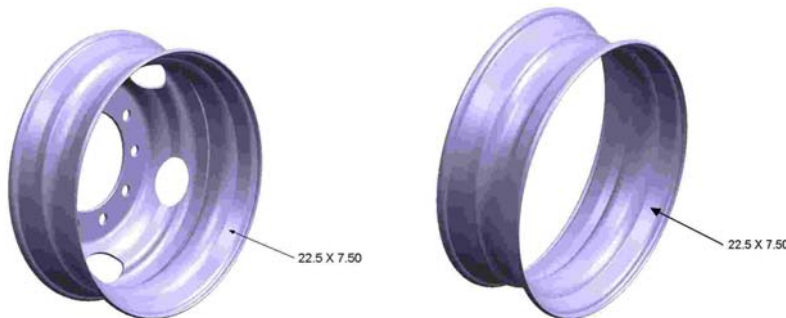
Roue : Indique l'emplacement de l'estampe de dimensions des roues d'acier et d'aluminium.
